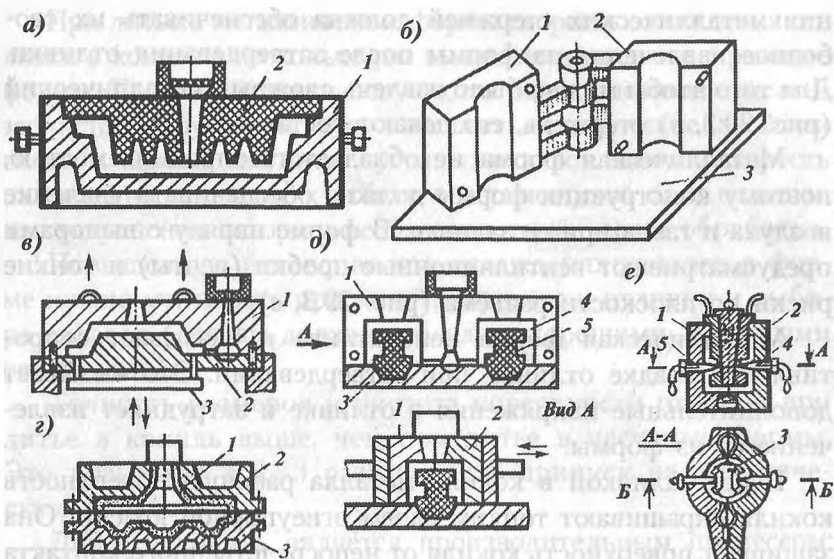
Примеры конструкций кокилей: а — неразъемный: 1 — кокиль; 2 — песчаный стержень; б — створчатый: 1, 2 — матрицы кокиля; 3 — плита; в — с горизонтальным разъемом: 1 — верхняя матрица; 2 — нижняя матрица; 3 — плита толкателей; г — облицованный: 1 — оболочка; 2, 3 — матрица; д — с вертикальным разъемом: 1, 2 — левая и правая матрицы; 3 — плита; 4 — полость формы; 5 — песчаный стержень; е — разъемный с металлическими стержнями: 1, 2 — матрицы кокиля; 3, 4, 5 — металлические стержни
